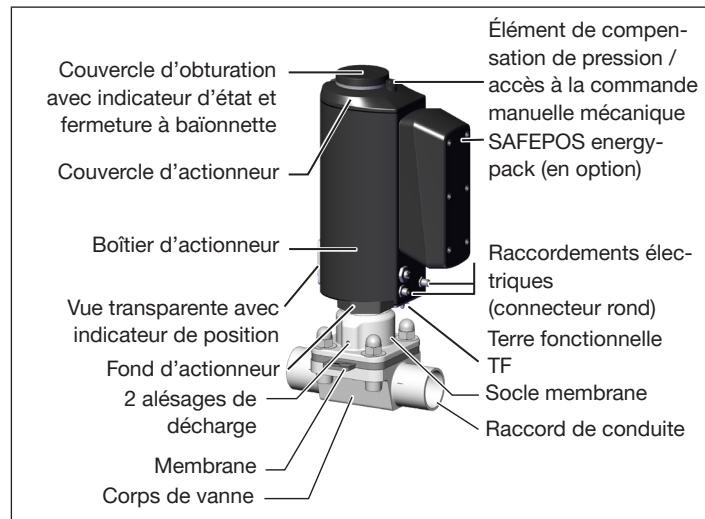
Assemblage, vanne à membrane électromotrice type 3323 AG3
